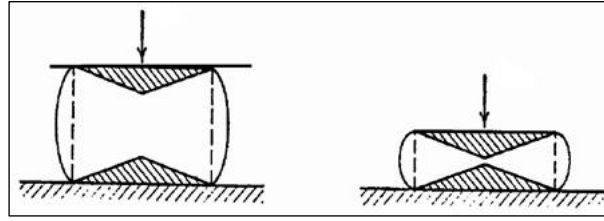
Abarillamiento de una probeta cilíndrica durante el ensayo de compresión.
